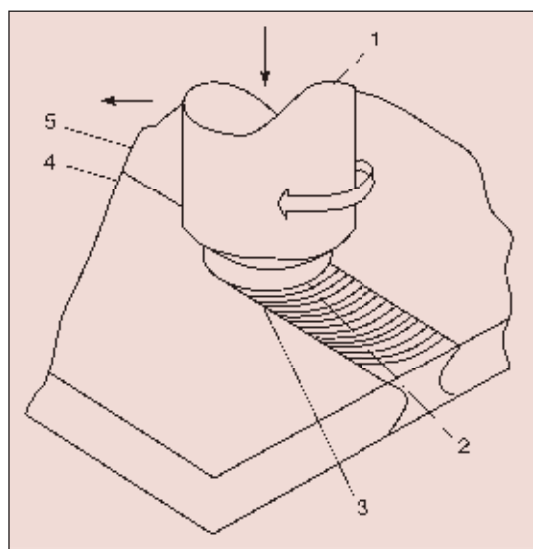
Схема сварки трением с перемешиванием алюминиевых сплавов: 1 — вращающийся инструмент; 2 — рабочая поверхность бурта инструмента; 3 — сварной шов; 4 и 5 — свариваемые детали
